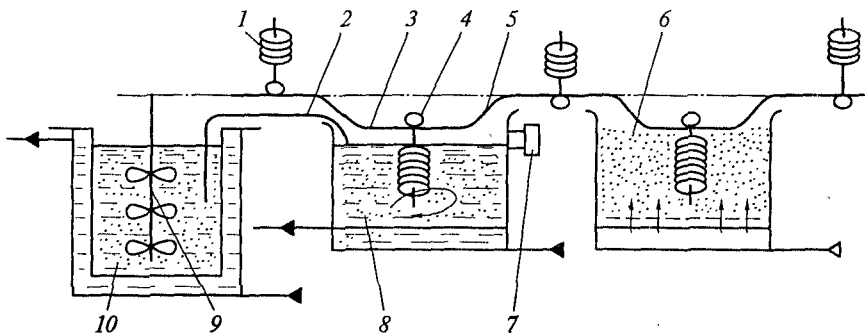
Схема агрегата для нанесения суспензии на блоки моделей и обсыпки их песком:
